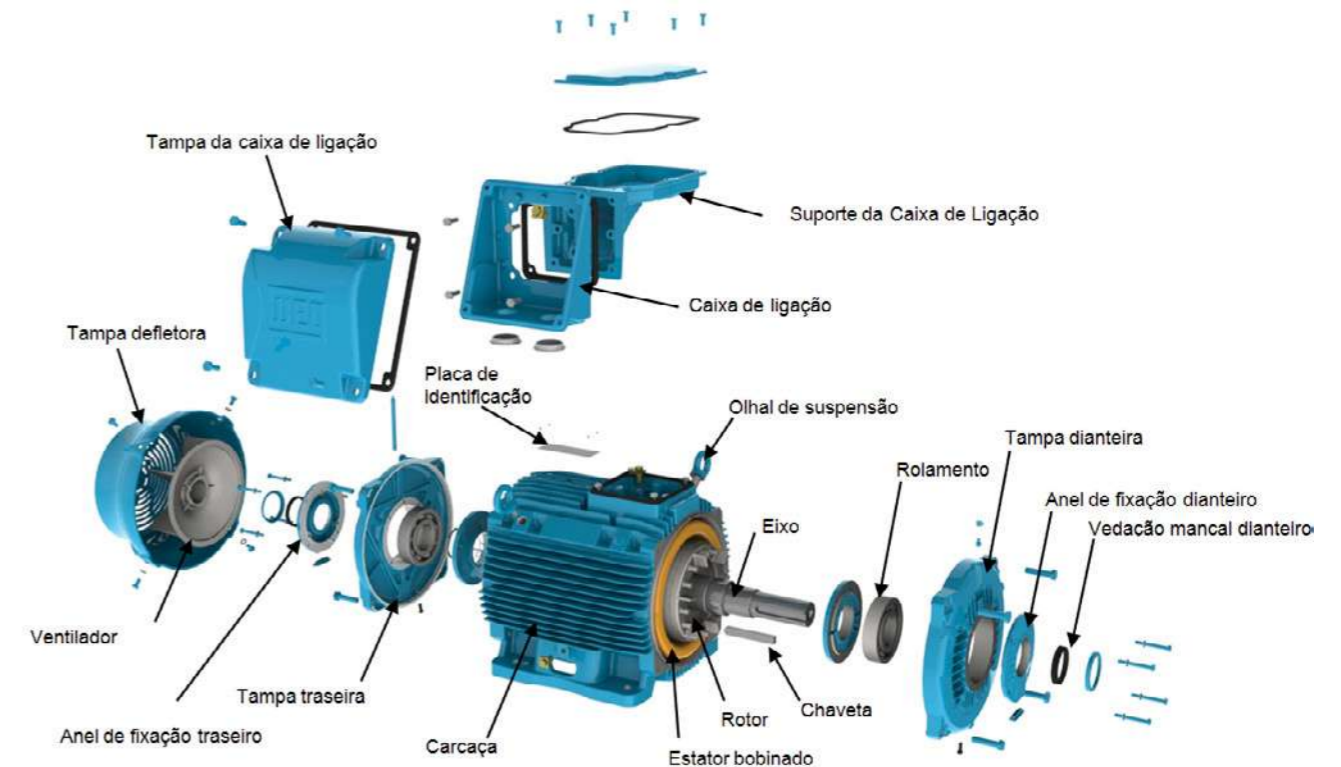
Vista explodida dos componentes de um motor com tipo de proteção "ec".
